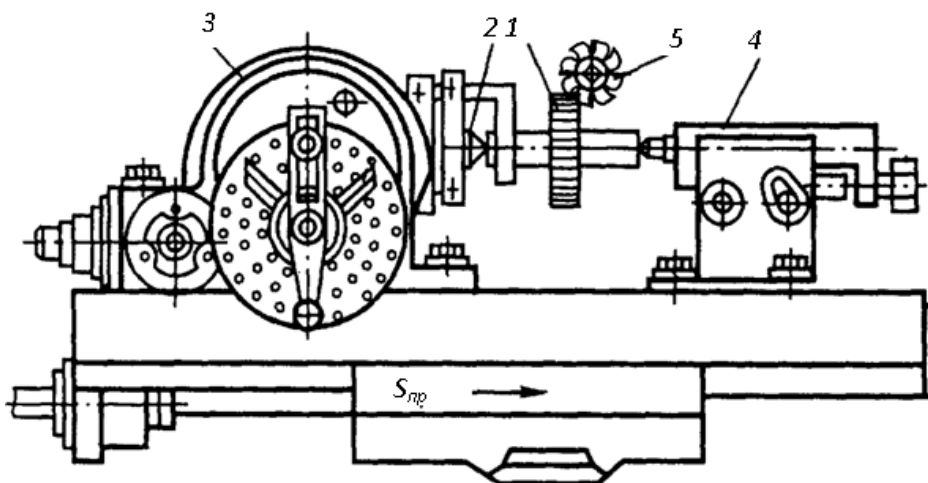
Схема обработки зубьев колеса в делительной головке
